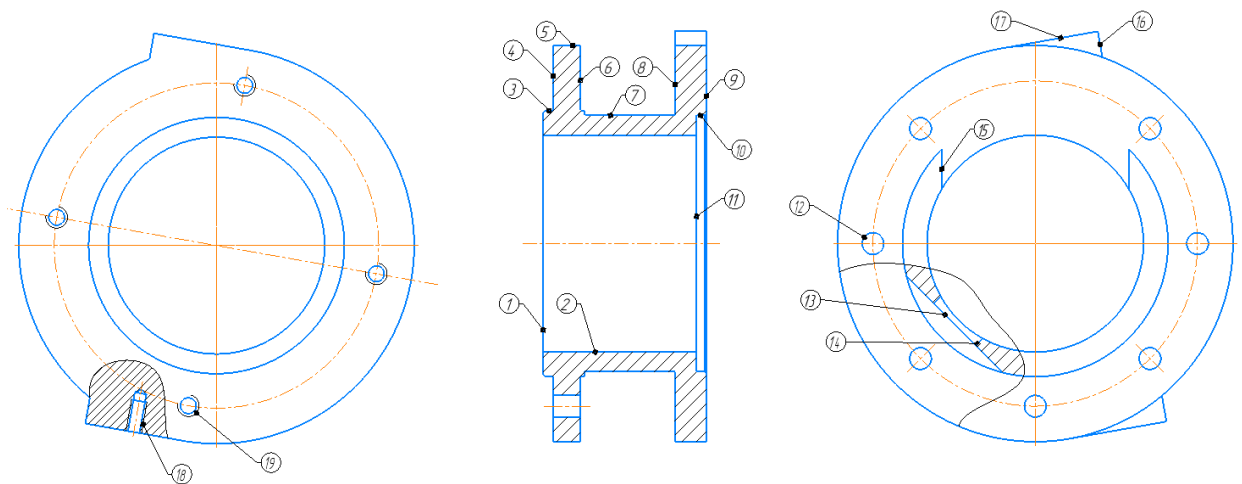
Технологічна розмітка поверхонь деталі
